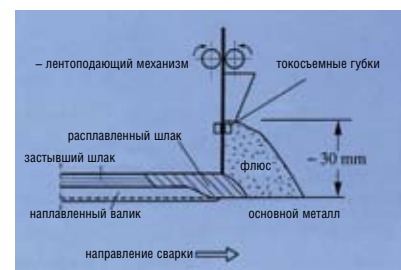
Принцип ленточной электрошлаковой наплавки.
